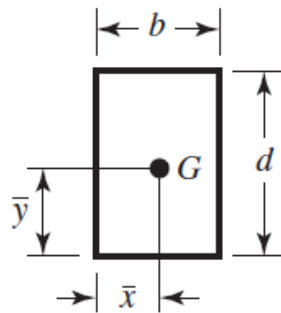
Perfil cordón de soldadura de contorno [23]
